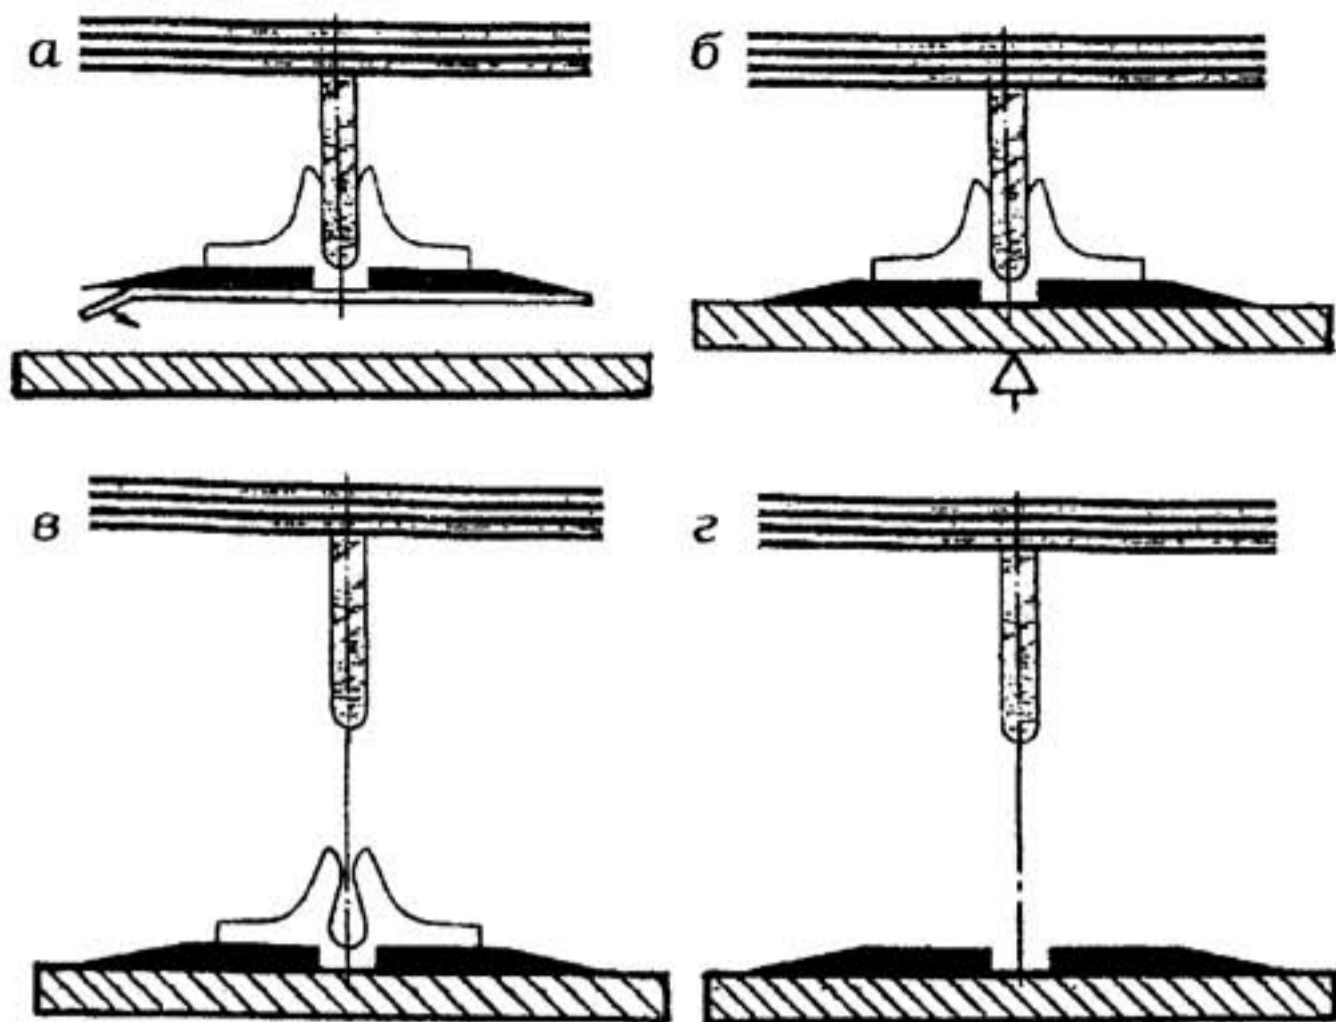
Схема изготовления контрштампов из пластмассовых биговальных матриц с юстировочными направляющими:
